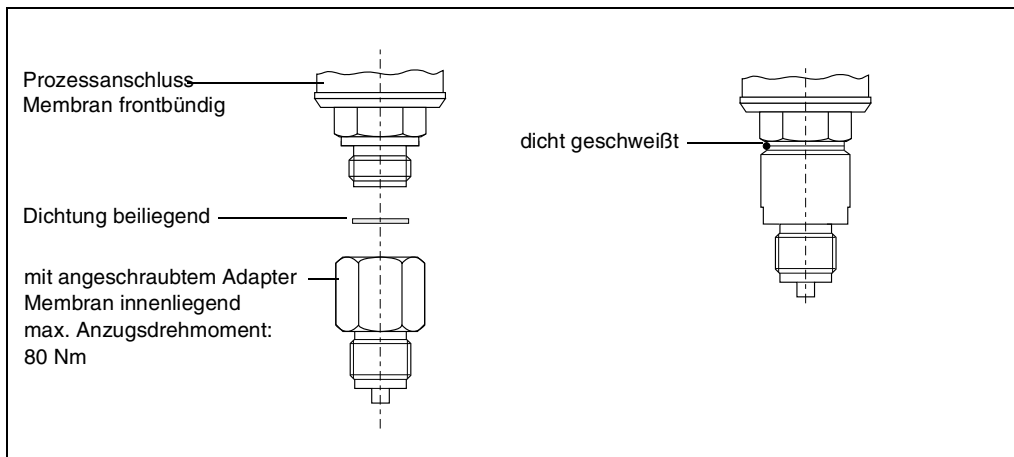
Barcon PPC-M10 mit angeschraubtem oder geschweißtem Adapter. Bei angeschweißtem Adapter max. Anzugsdrehmoment 80 Nm
